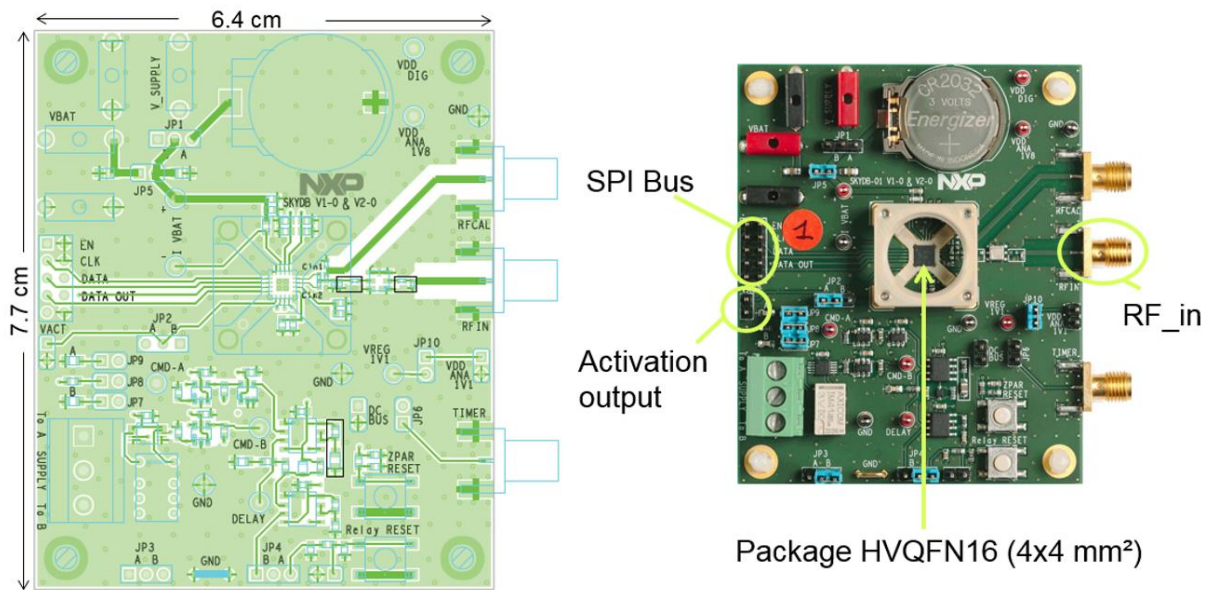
Vue top du layout du PCB à gauche et sa photo une fois monté à droite
